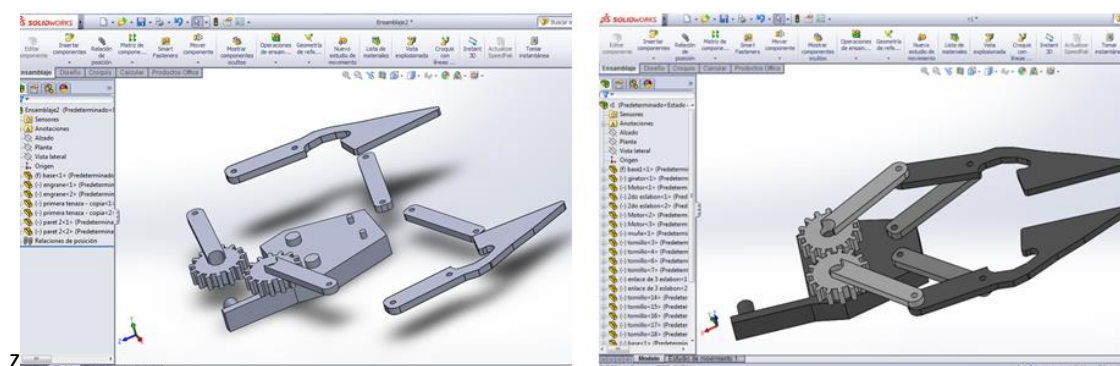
Izquierda: piezas antes de ensamble, Derecha: Ensamble y adición de color (Ensamble 4).
